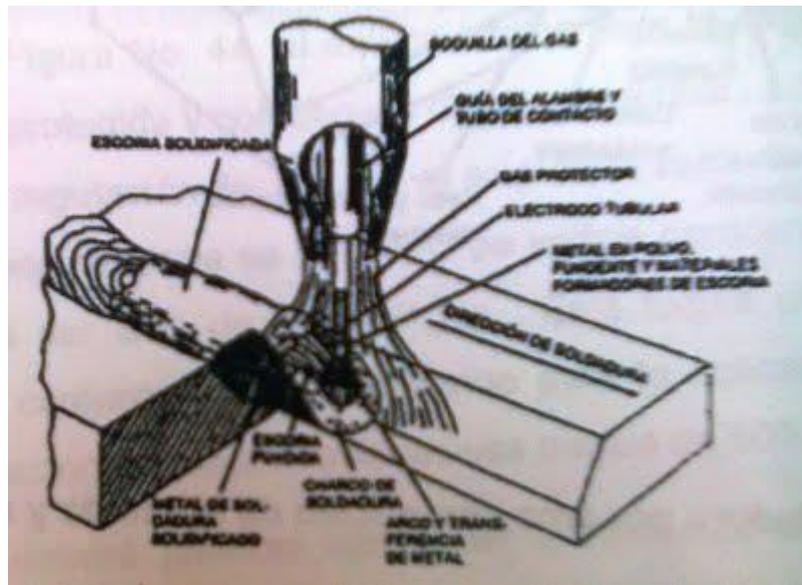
Soldadura por arco con núcleo de fundente con gas.
